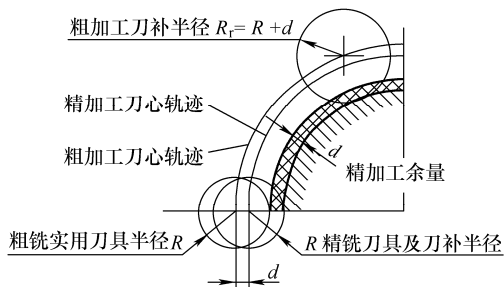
利用修改刀具半径补偿实现零件粗、精加工
